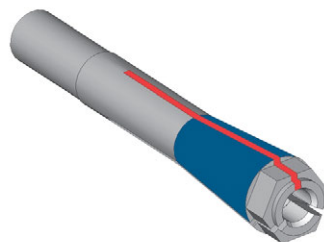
ENGRASAR LA PINZA DE SUJECIÓN; LA SUPERFICIE A LA QUE SE DEBE APLICAR GRASA APARECE MARCADA EN AZUL; LA RANURA QUE NO DEBE ENGRASARSE APARECE MARCADA EN ROJO
